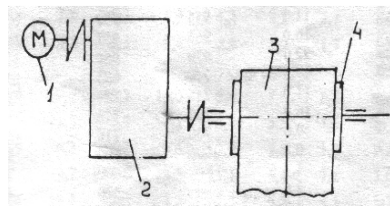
Схема привода конвеєра: 1 - двигун; 2 - редуктор; 3 - стрічки; 4 - барабан.
